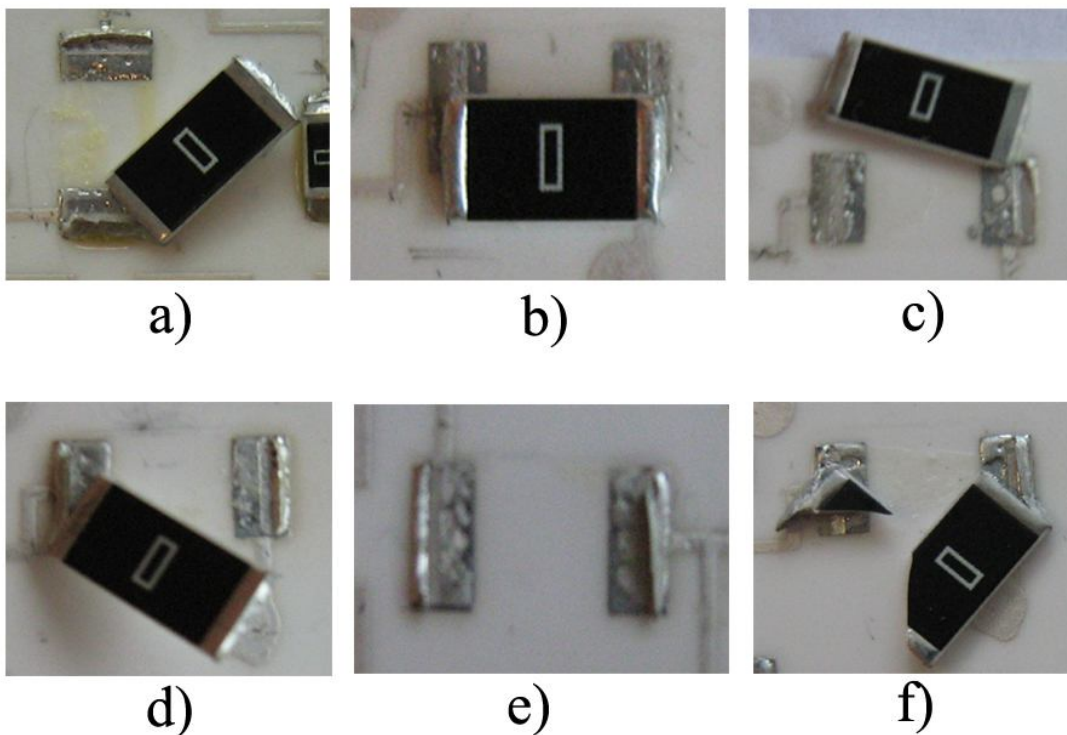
Detailní pohled na zapájený rezistor typu 0402, pájeno na vzduchu, pasta Sn62Pb36Ag2.
